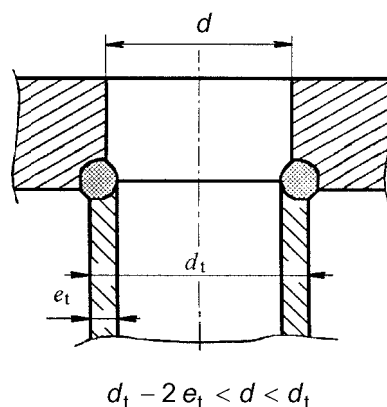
Tubos parcialmente insertados soldados a la cara interior de la placa de tubos
